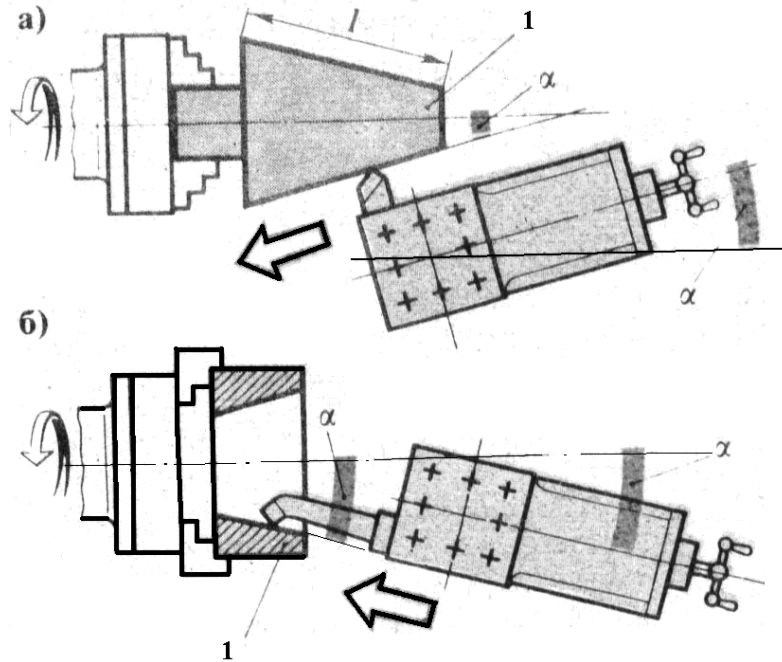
Обробка конічних поверхонь при повернутих верхніх полозках супорта: а – обточування зовнішньої поверхні, б – розточування внутрішньої поверхні, 1 – заготовка
